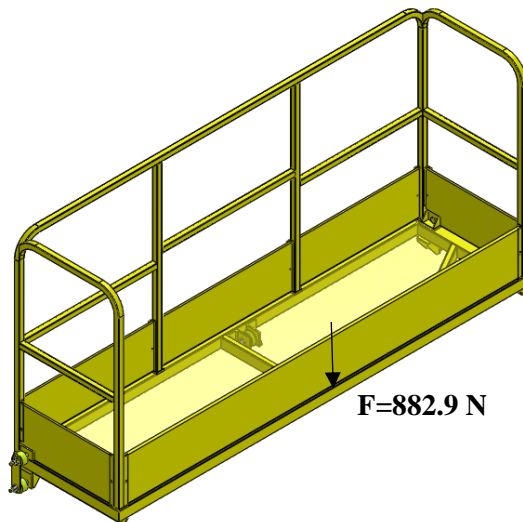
Aplicación de la F en el centro de la estructura de la canasta de elevación
